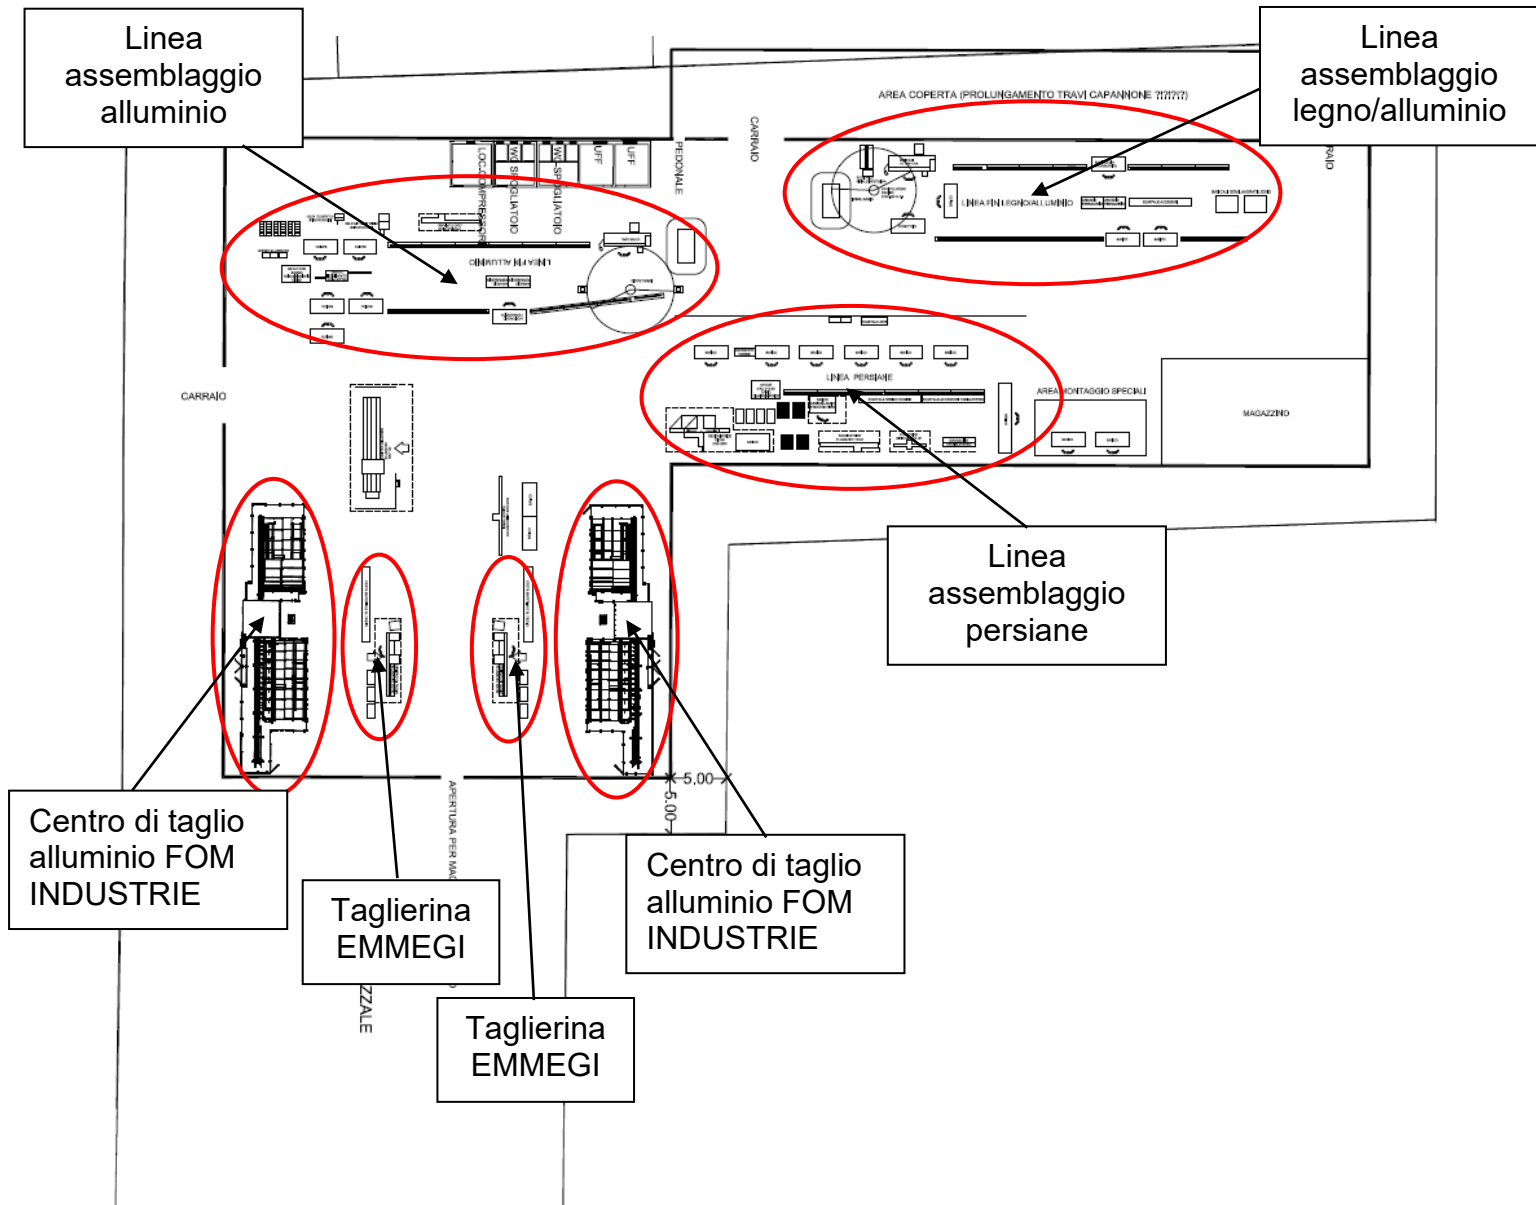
Planimetria generale dell'unità 3 in progetto;
